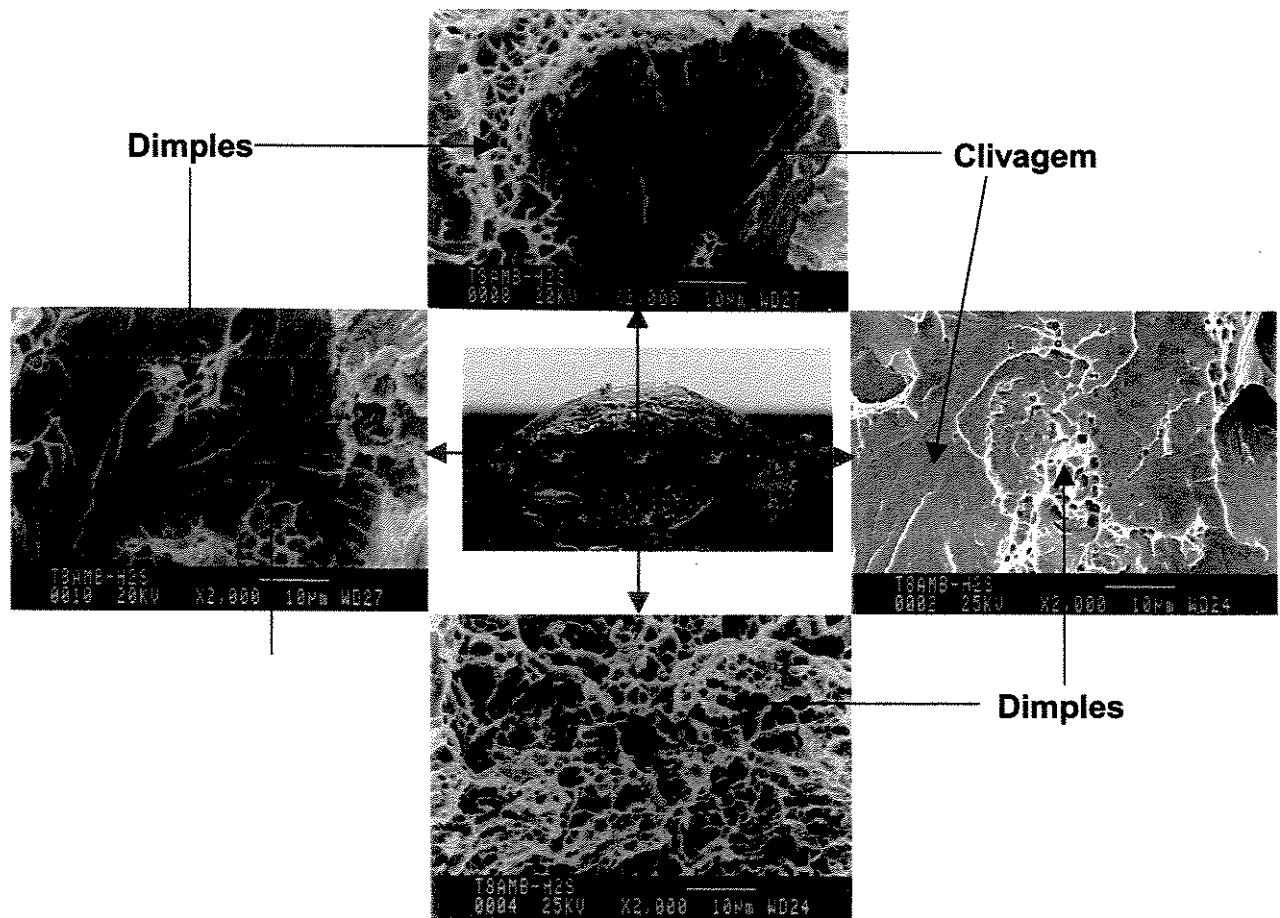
Superfícies de fratura da trinca de hidrogênio do metal de solda do arame E71T8-K6 exposto ao H₂S
